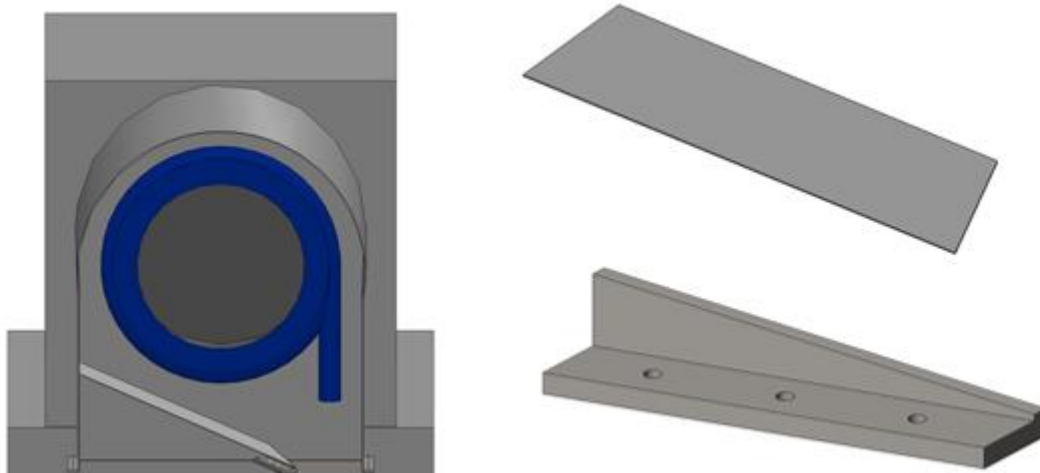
Detalle de la chapa soldada en el interior de la tolva de la centrífuga y del soporte diseñado para el apoyo de esta.
